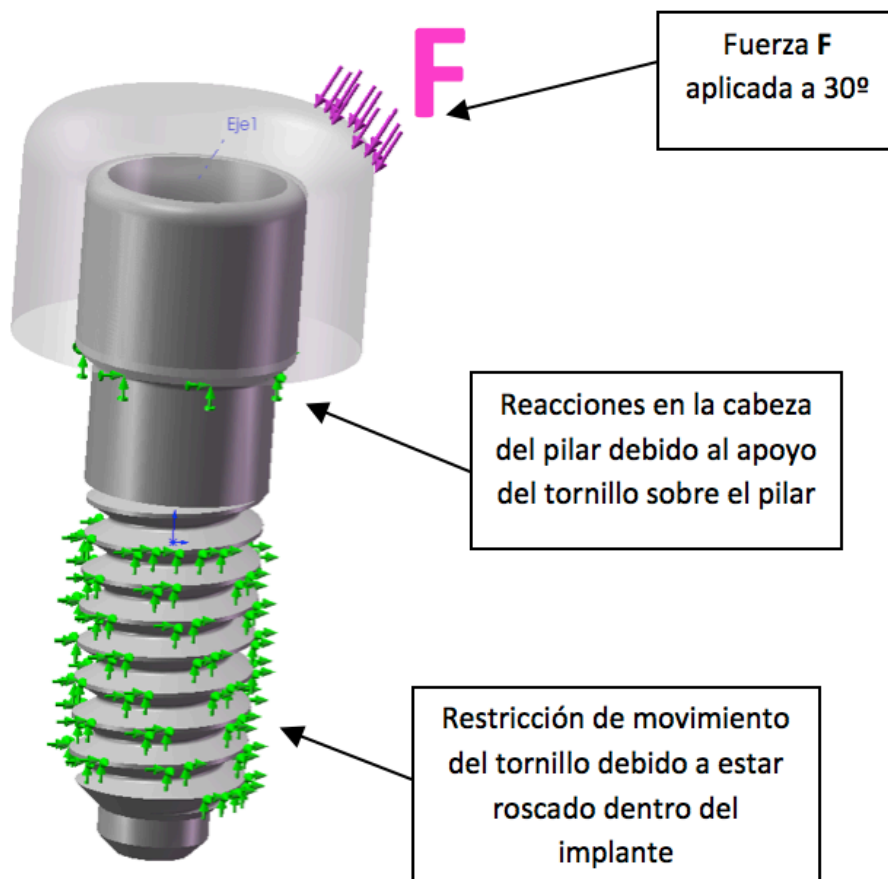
Esquema del diseño del ensayo mediante AEF del tornillo prototipo 1.
